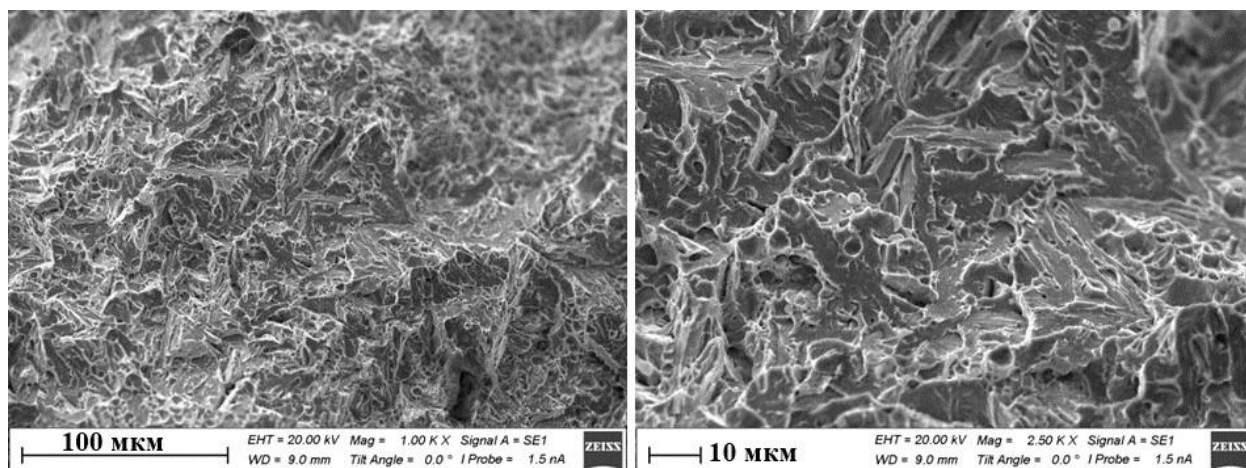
Структура хрупкого излома наплавки №2
